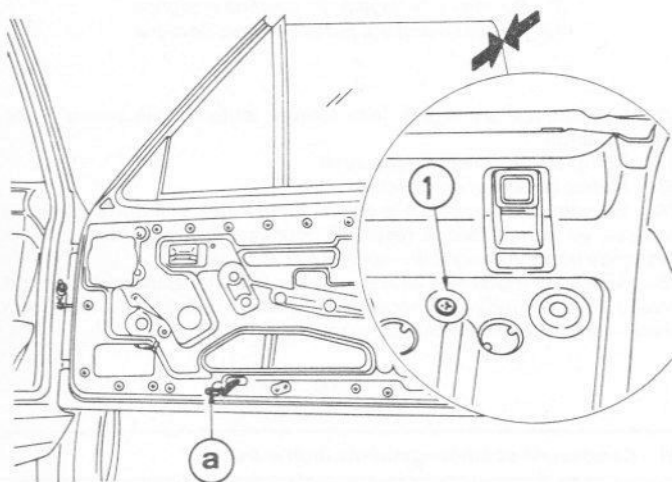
Vis de réglage du bord arrière de la glace de porte (1) – modèles Cabriolet (Sec 21)
